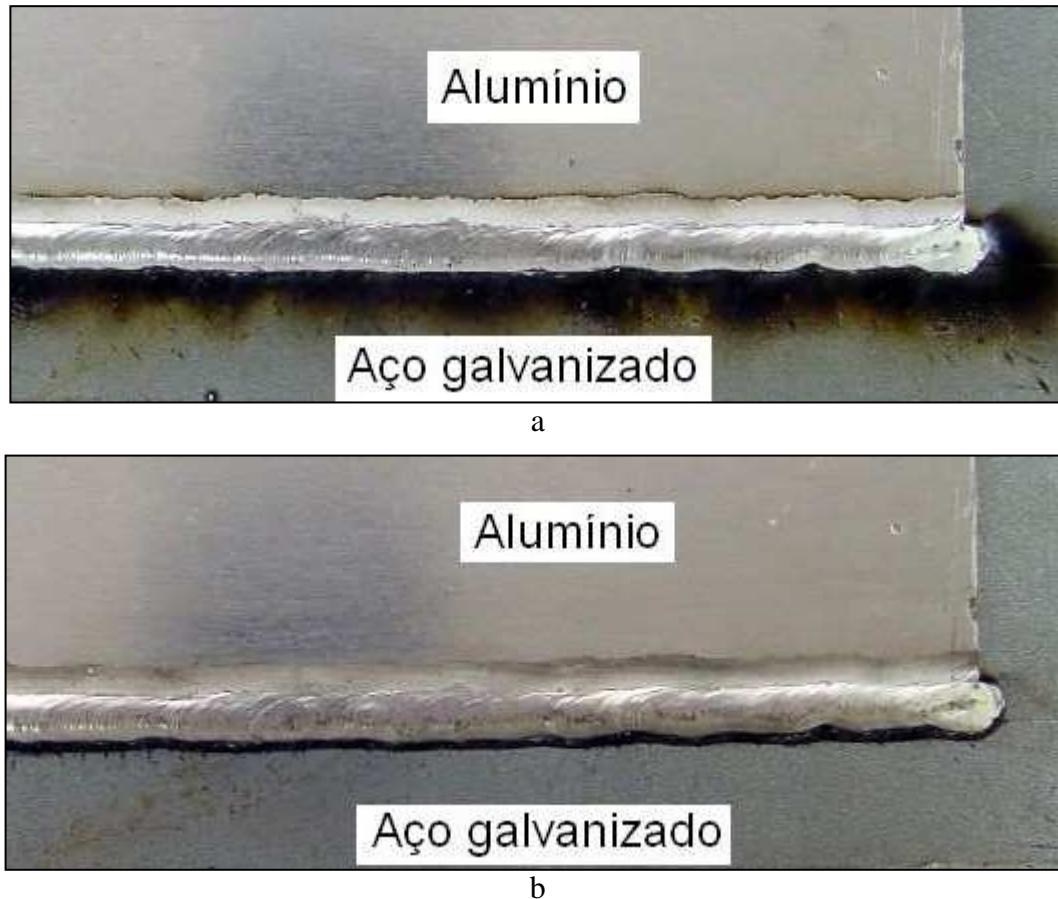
Brazagem MIG CA – Alumínio & Aço (galvanizada); (a) aspecto após soldagem (b) aspecto após remoção de fuligem
